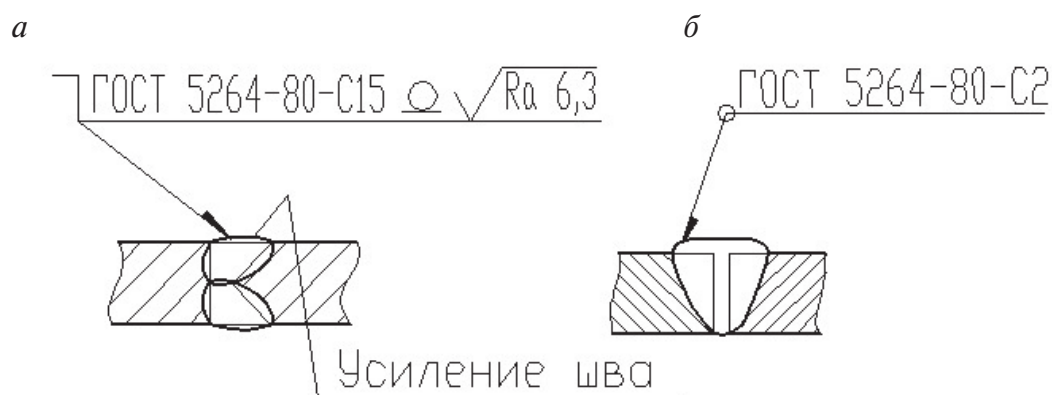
Примеры обозначения стыкового сварного шва:
